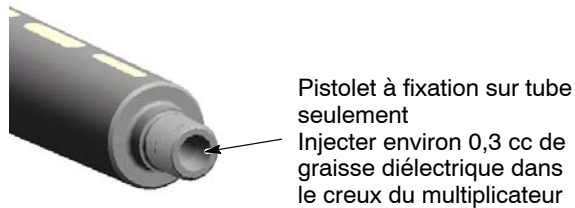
Graissage du creux du multiplicateur – pistolet à fixation sur tube
